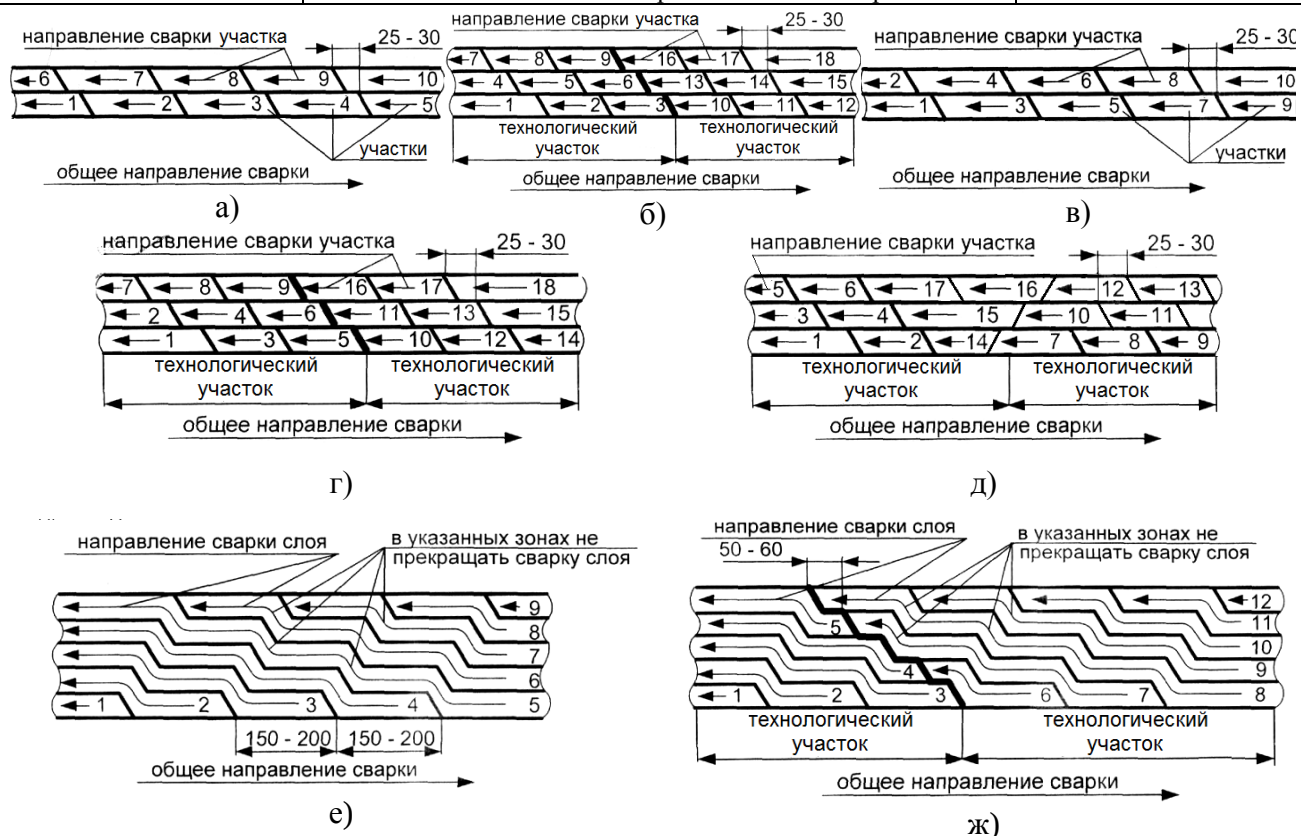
Способы выполнения швов сварных соединений
